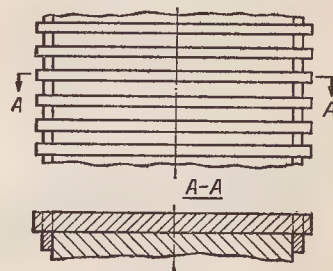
Сварка стержней и короткозамыкающих колец у ротора дугостаторной машины
